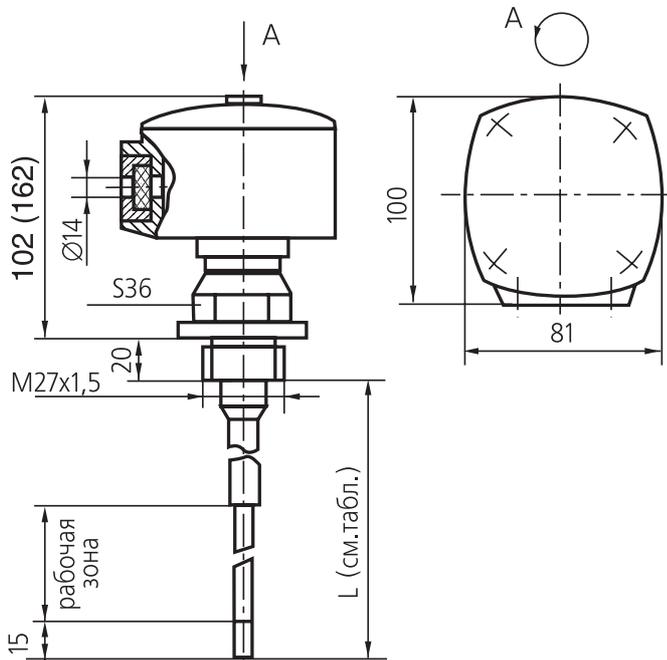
Общий вид, габаритные и установочные размеры СУС 113Р(Б)
